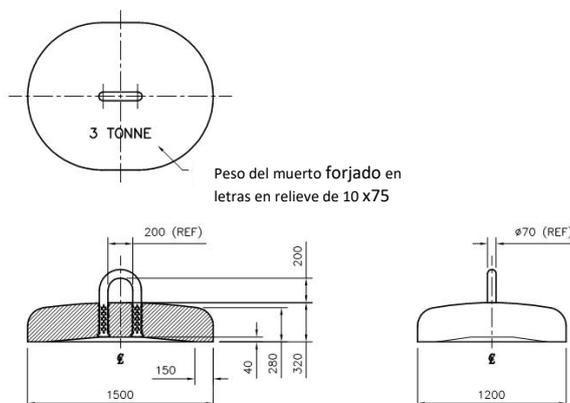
Muerto de hierro fundido de 3 toneladas de Trinity House
